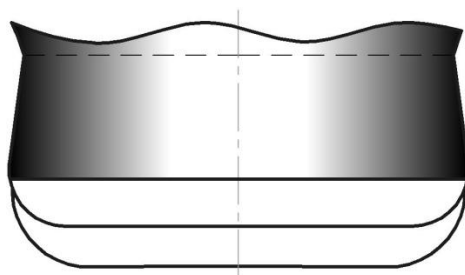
Форма поверхности среза вырубленной детали при большом зазоре.
